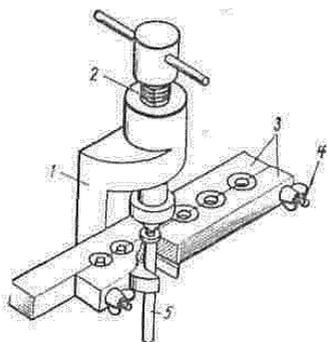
Приспособление для развальцовки концов топливопроводов:
